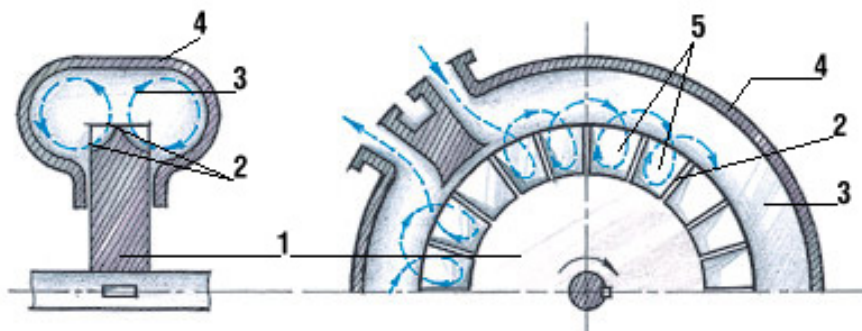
Схема вихревого насоса: 1 — рабочее колесо; 2 — лопатка;
